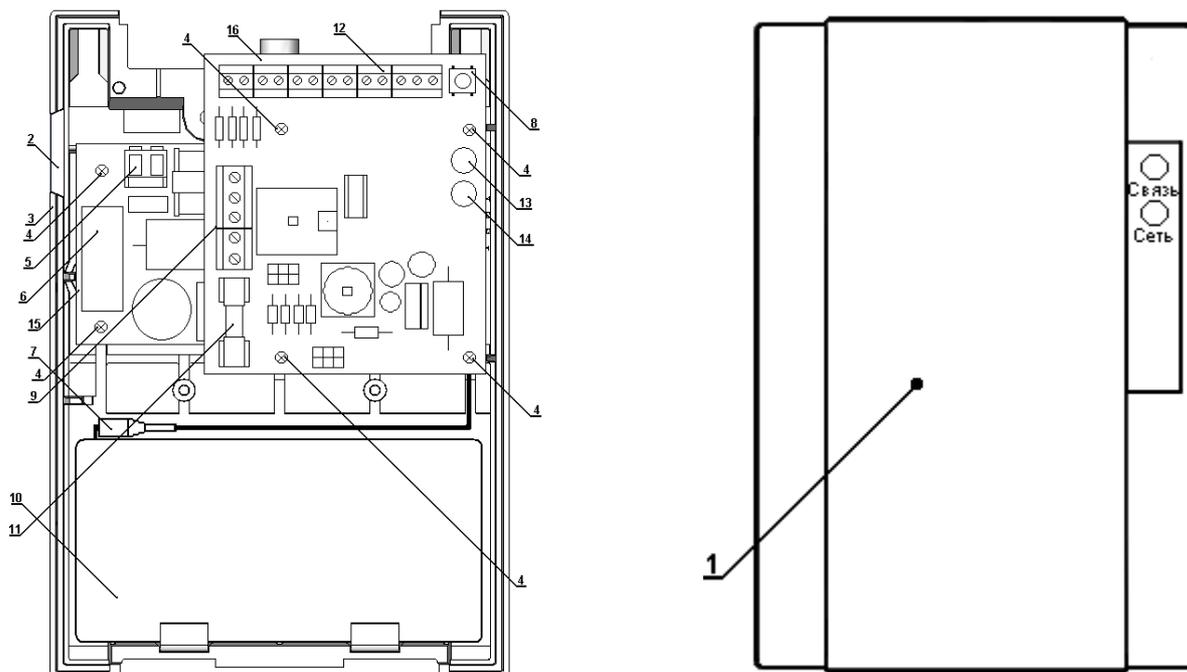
Внешний вид контроллера «Кронверк АТ-02».
